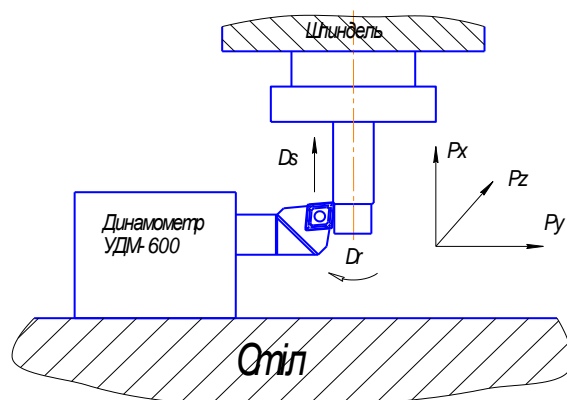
Схема вимірювання сили різання на фрезерному верстаті
